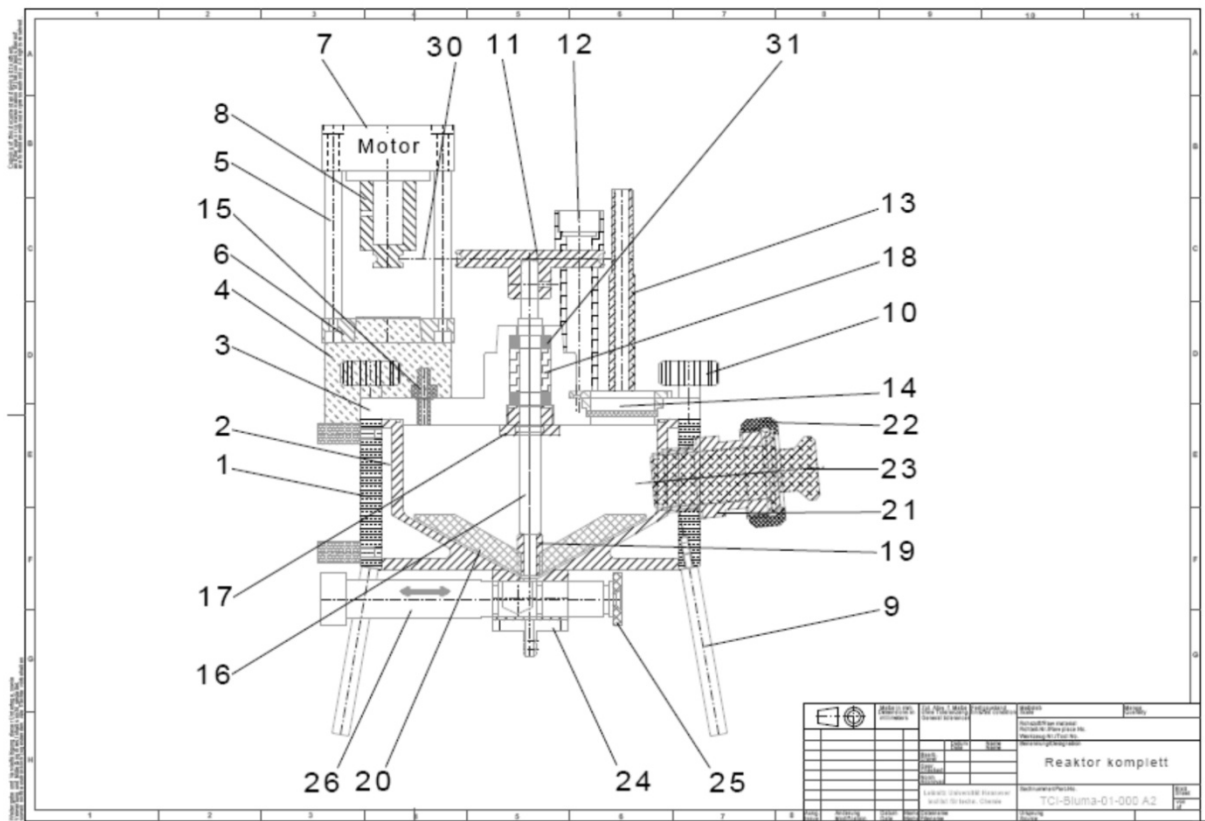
Technische Zusammenbauzeichnung des Prototypen B.
